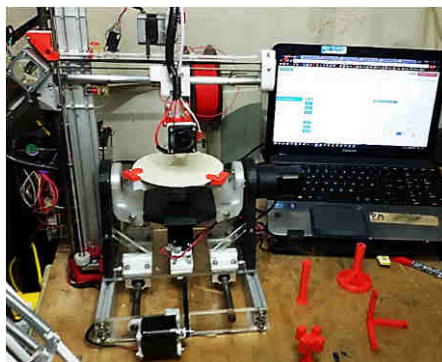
Montaje final del prototipo de impresión 3D de cinco ejes
